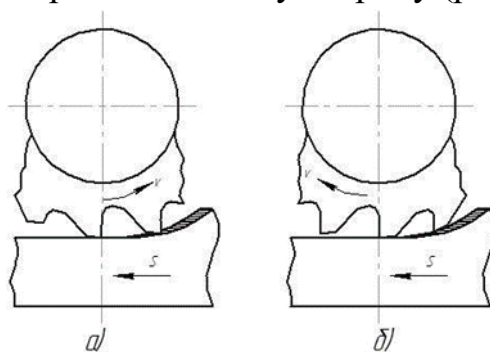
Два метода фрезерования: а – встречное; б – попутное
